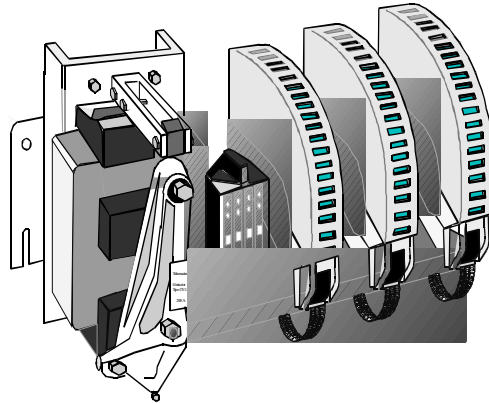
VISTA FRONTAL DE UN CONTACTOR DE ROTACIÓN
